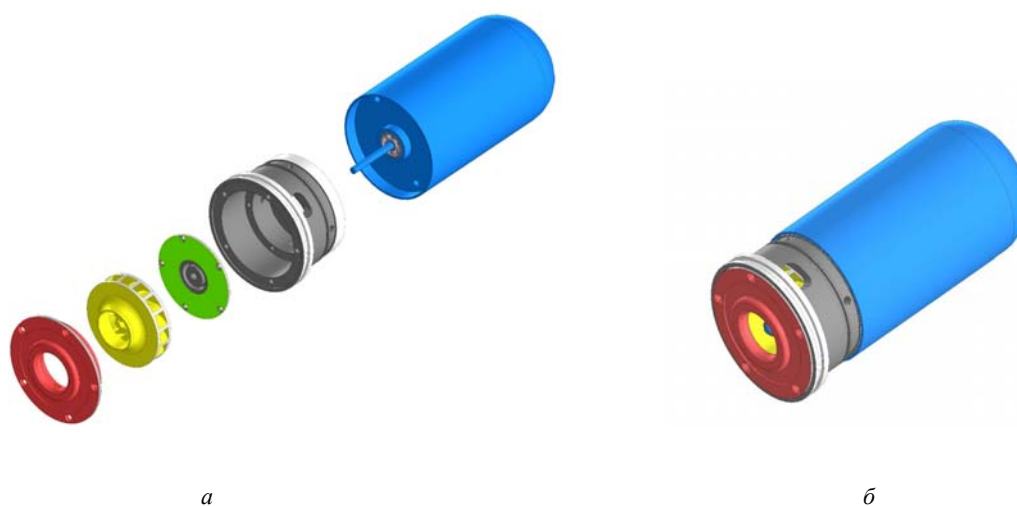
Конструкция топливного насоса с коллекторным двигателем:
